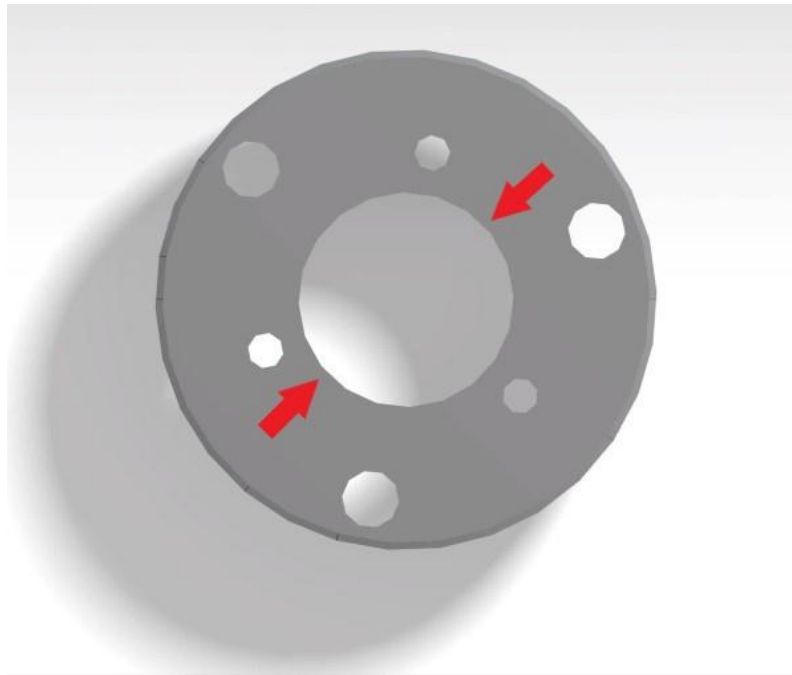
Vista en detalle del taladrado central de la base (Fuente: elaboración propia)
